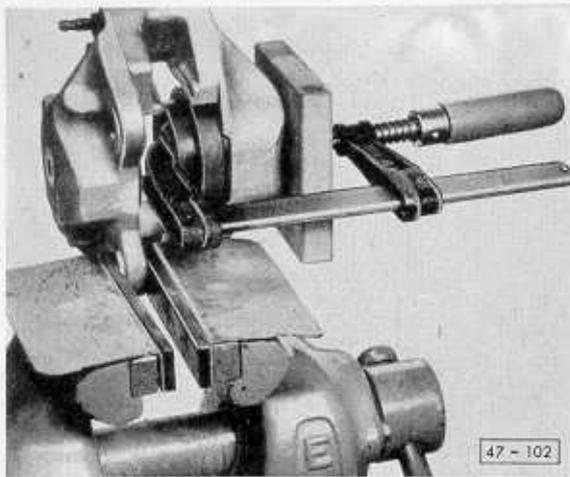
Schutzkappe mit Druckstück VW 442 sorgfältig auf den Sitz des Gehäuses drücken. Dabei wird gleichzeitig der Kolben ganz eingedrückt.
